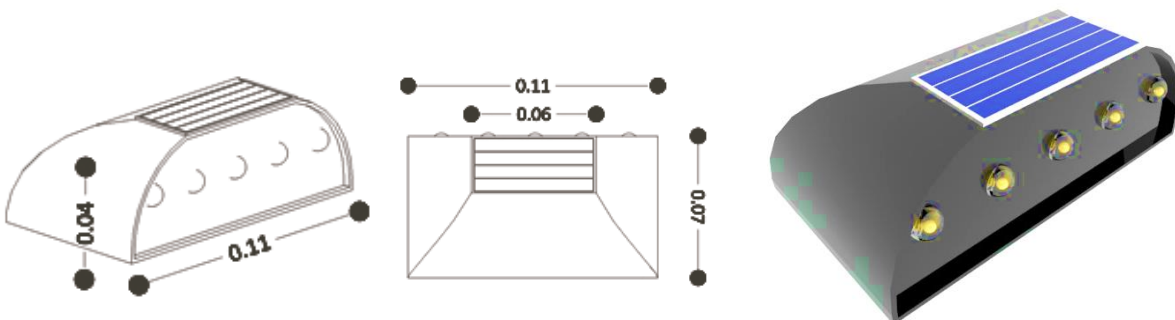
Planimetría y render, reflector de piso. Fuente: grupo de investigación.
